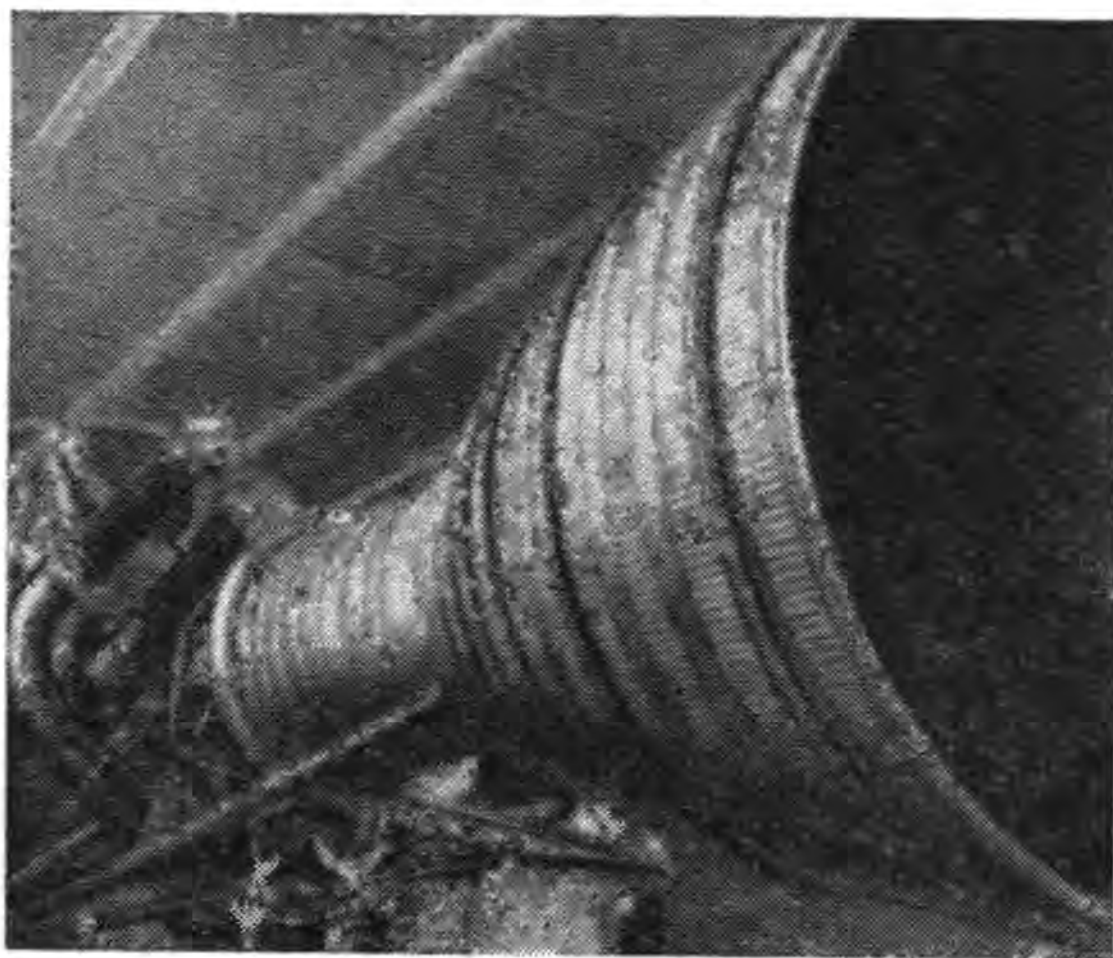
Камера сгорания современного ракетного двигателя, изготовленная пайкой
